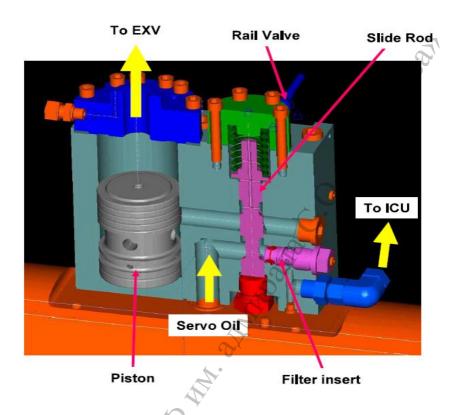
Valve control unit (VCU) - Модуль управления клапанами: То ICU) - Впрыска и То EXV - Выхлопа: Rail valve (RV) — Клапан в топливную в магистраль, Piston — Поршень, Slide Rod - Скользящий шток, Filter insert — Фильтр «входящего» масла
